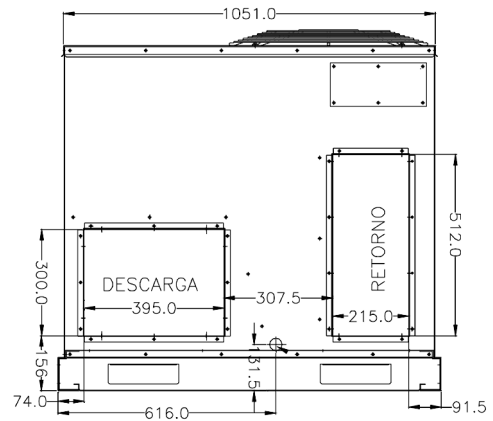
Aperturas para Conducto de Inyección y Retorno Horizontal
